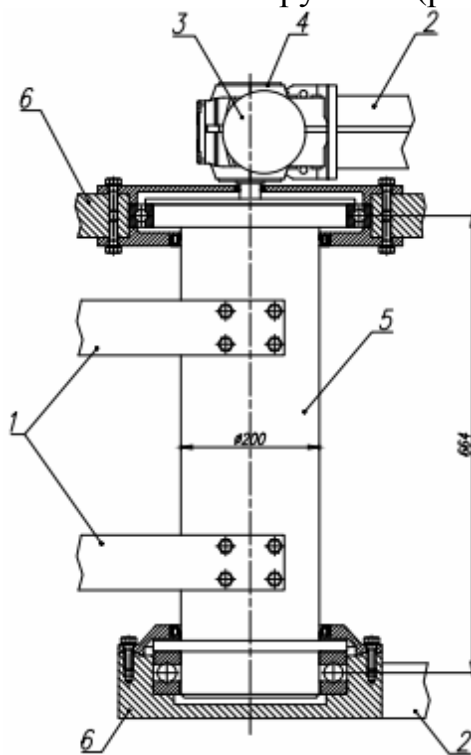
Поворотный механизм: 1, 2 – тяги крепления, 3 – гидромотор, 4 – червячный редуктор, 5 – распределительный вал, 6 – опорные подшипники
